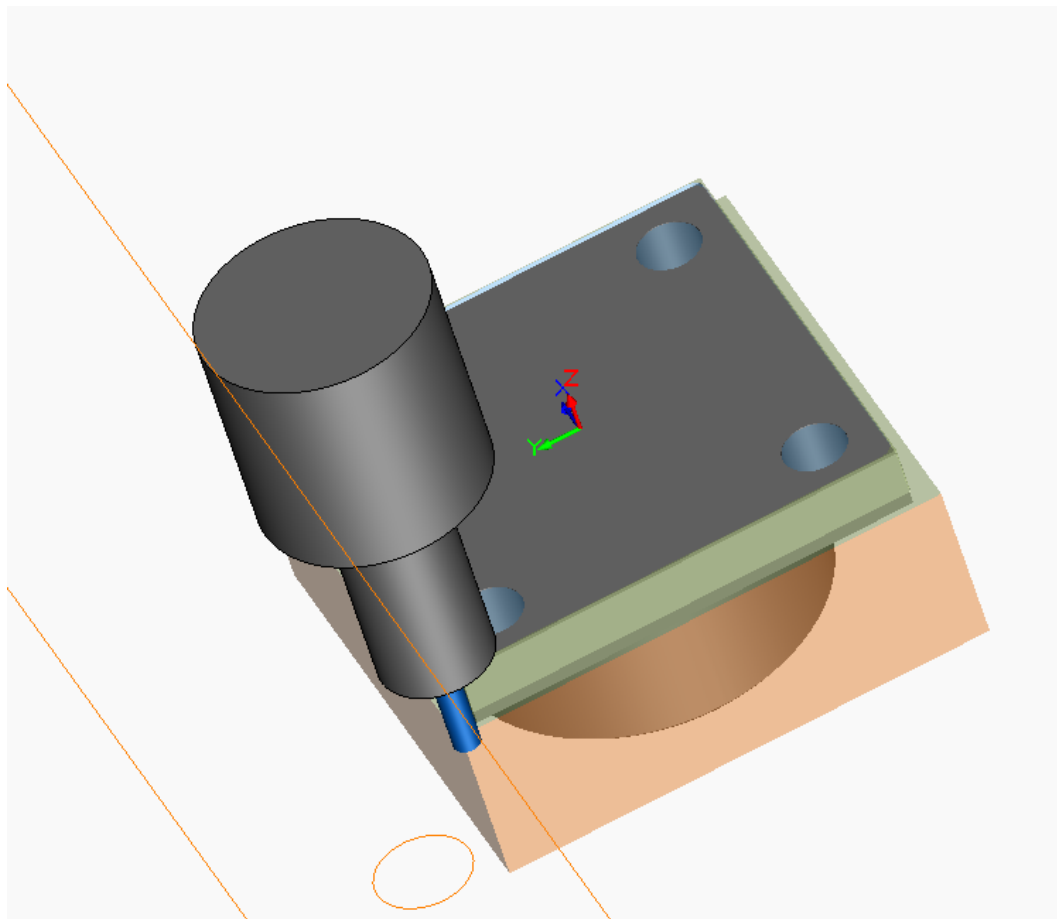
Симуляція обробки деталі на фрезерному верстаті (точіння поверхні 4)
